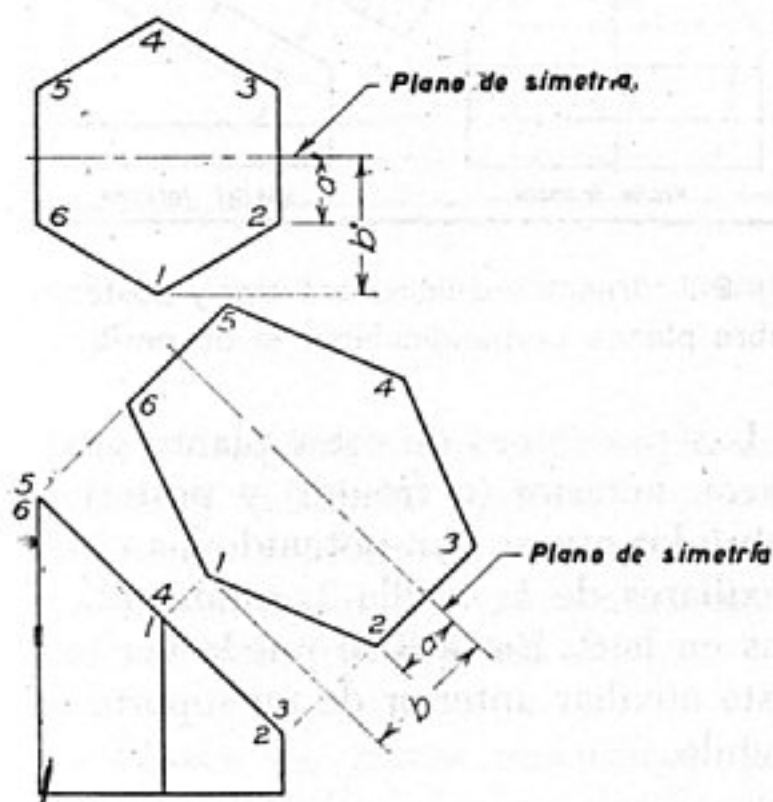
Vista auxiliar a partir de un plano de simetría.
